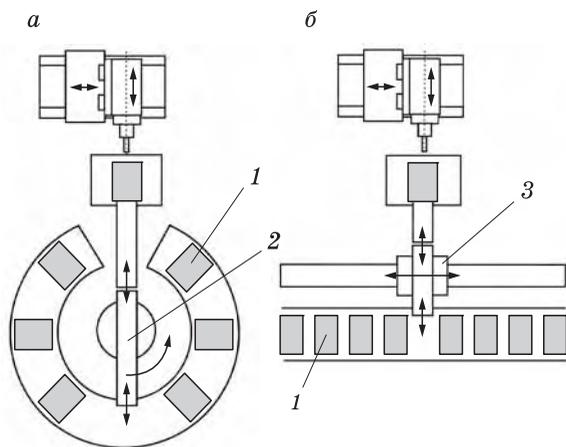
Неподвижные магазины палет, используемые в ГПМ для обработки корпусов:
